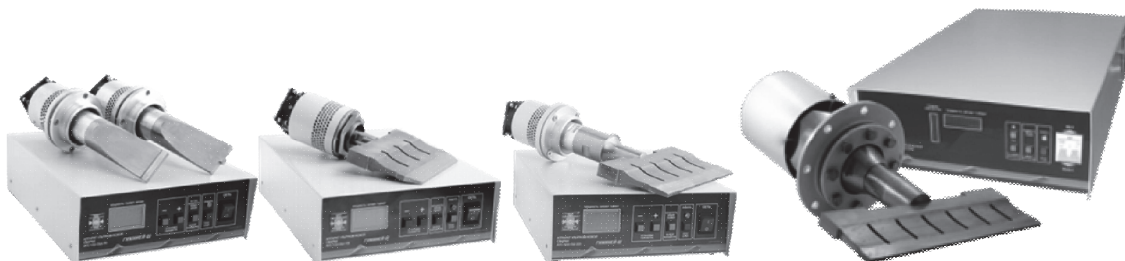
Сварочные аппараты для прессовой сварки линейных швов
